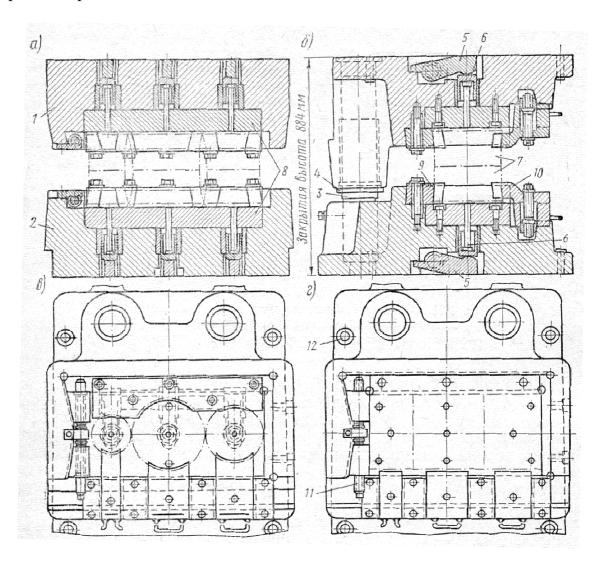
Схема универсального штампа для горячей штамповки на кривошипном горячештамповочном прессе усилием 20 000 кН: а – разрез параллельно фронту пресса; б – разрез перпендикулярно фронту пресса;
